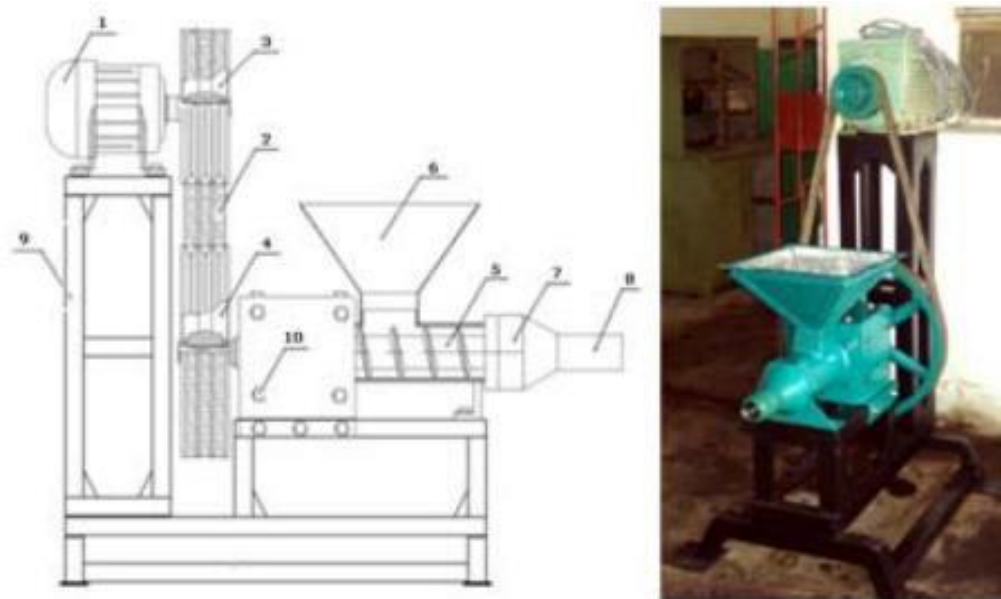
Esquema de la máquina briquetadora experimental por extrusión. Fuente: “Impacto medioambiental en la construcción de una máquina briquetadora experimental por extrusión”.
